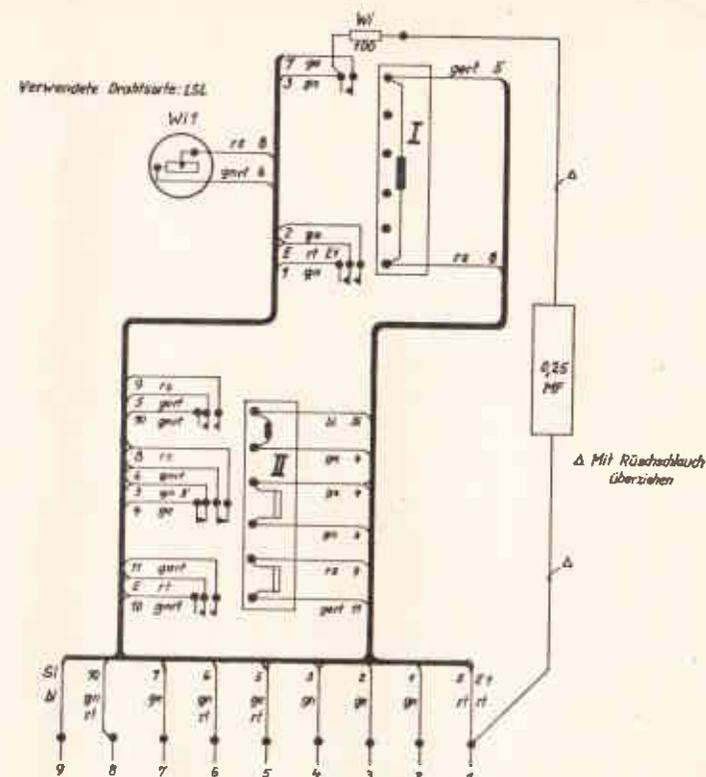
Beispiel einer Montagezeichnung: Relaisunterbrecher 50
